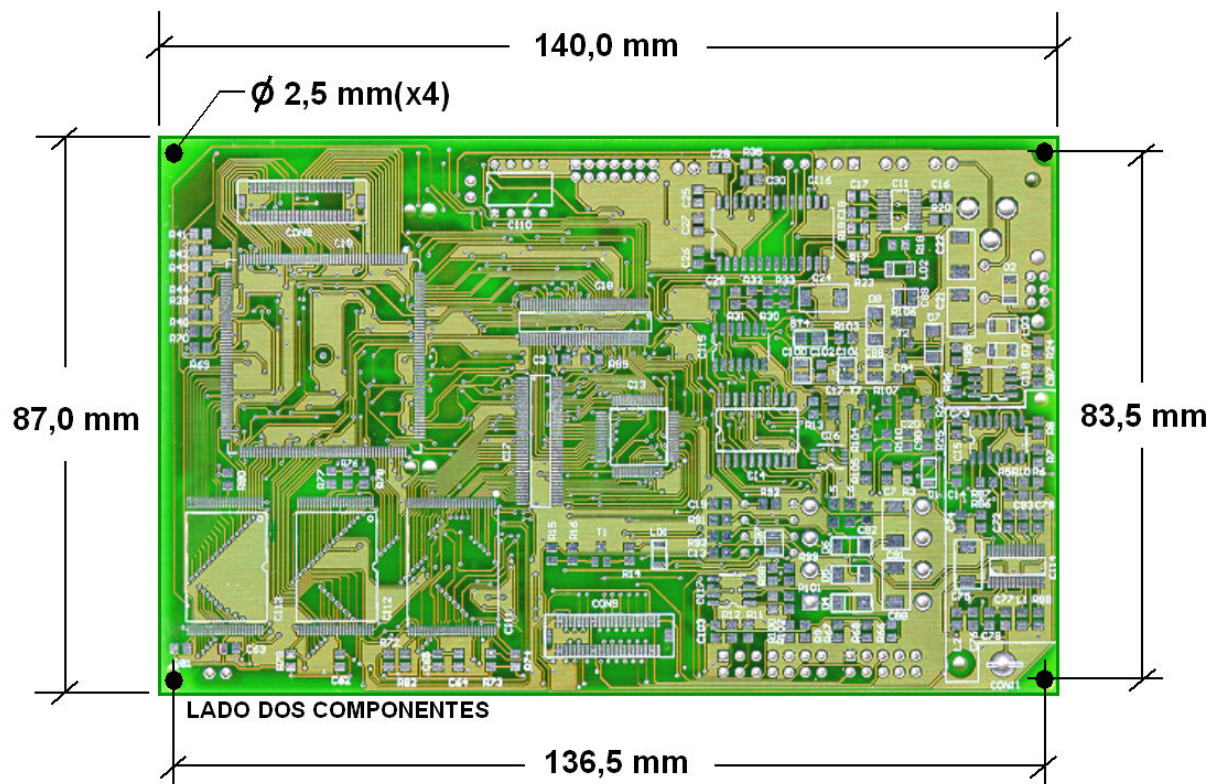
Detalhe das dimensões físicas do PCB do RANS-300.
